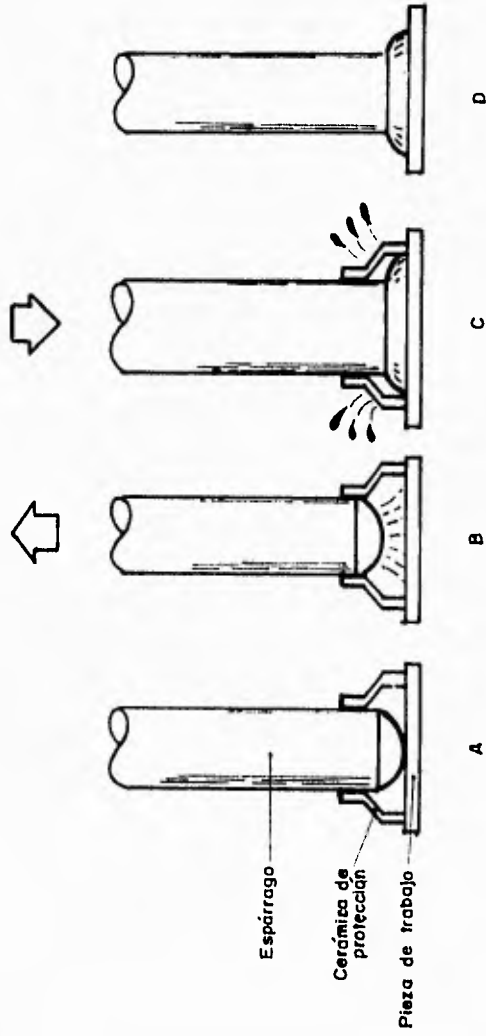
Soldadura por espárragos (SW)
